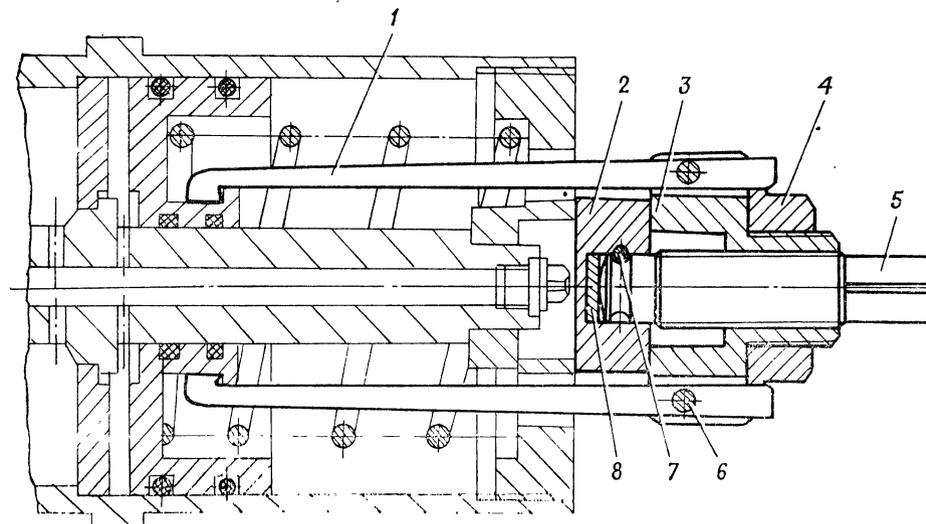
Установка приспособления 41.020 Сб для отгибания поршня компенсатора:
